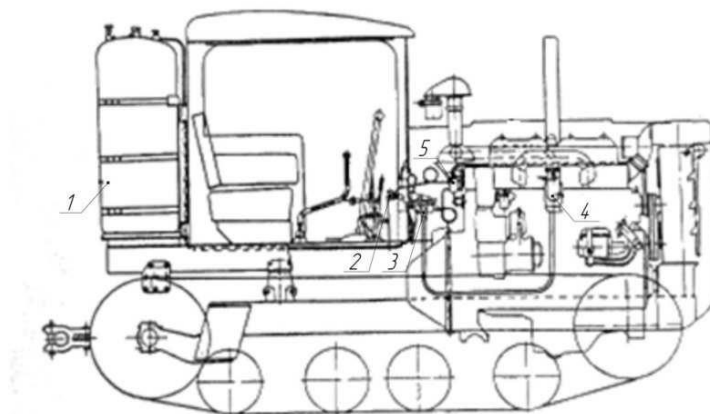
Схема розташування приладів системи живлення на газобалонному тракторі: 1 - газовий балон; 2 – магістральний вентиль; 3 – редуктор; 4 – змішувач; 5 - випарник
